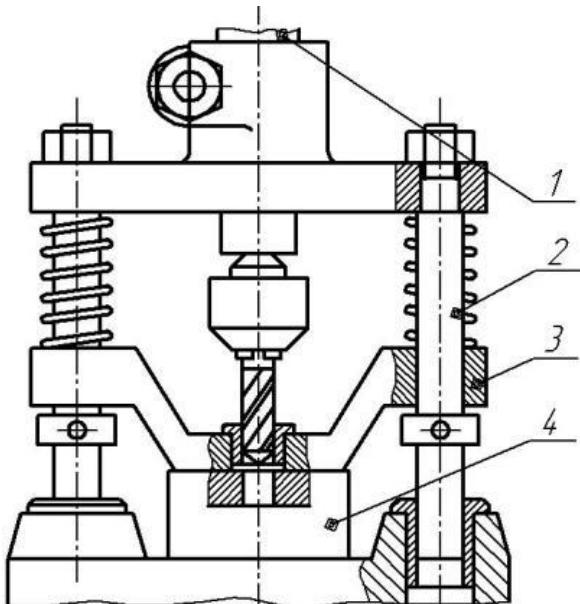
Схема автоматизированного пружинного зажима заготовки в сверлильном приспособлении:
